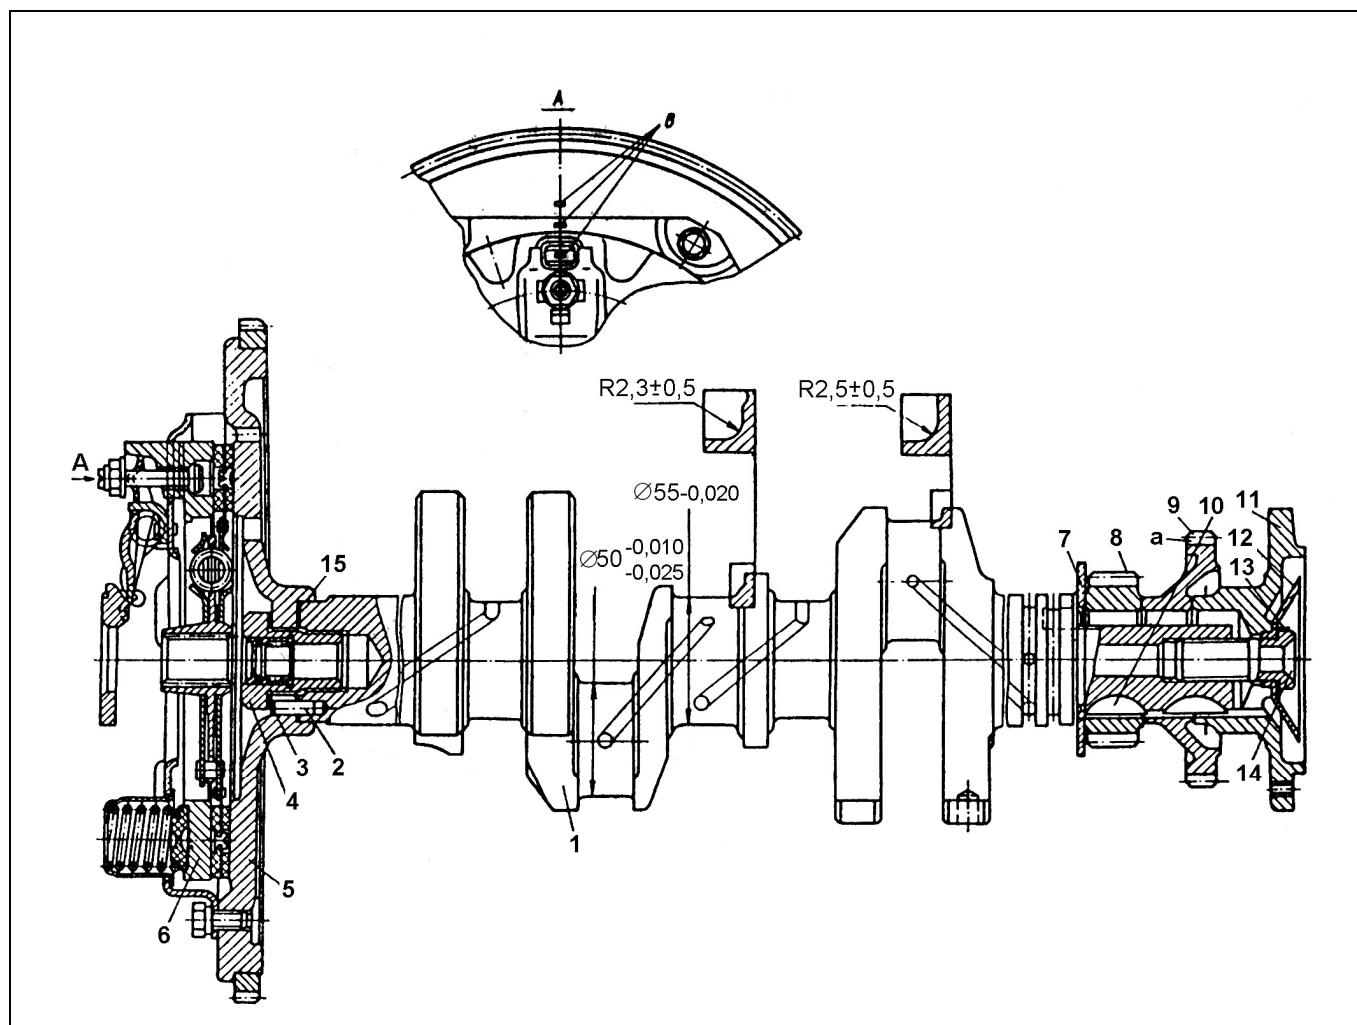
Коленчатый вал с маховиком и нажимным диском сцепления в сборе: 1 - вал коленчатый; 2 - штифт маховика; 3 - стопорная шайба; болт маховика в сборе; 5 - маховик в сборе; 6 - нажимной диск сцепления с кожухом в сборе; 7 - шайба опорная коленчатого вала; 8 - шестерня распределительная; 9 - шестерня привода уравнивающего механизма; 10 - шпонка сегментная; 11 - корпус центробежного маслоочистителя; 12 - маслоотражатель центробежного маслоочистителя; 13 - шайба отгибная; 14 - болт центробежного маслоочистителя; 15 - прокладка; В - метки.
